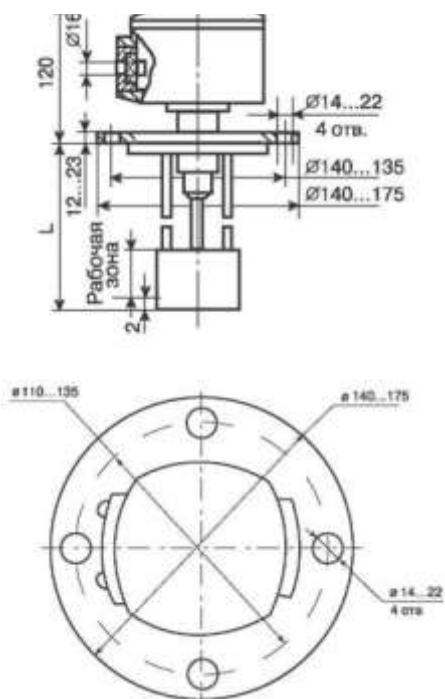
Общий вид, габаритные и установочные размеры СУС-171Р(Б)
